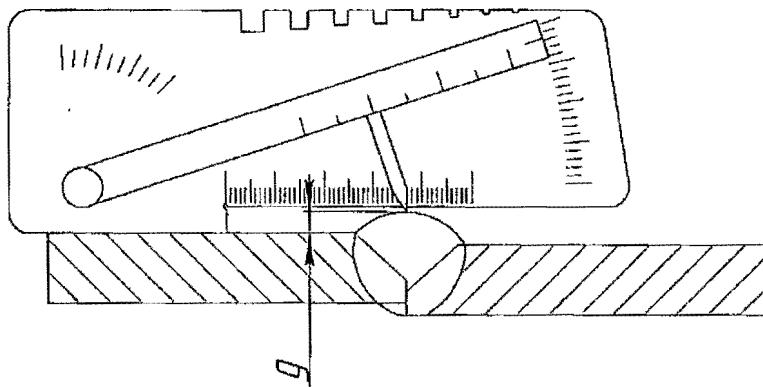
9. Измерение выпуклости (вогнутости) шва (g) сварного соединения при различном уровне наружных поверхностей деталей, вызванном смещением при сборке соединения под сварку
